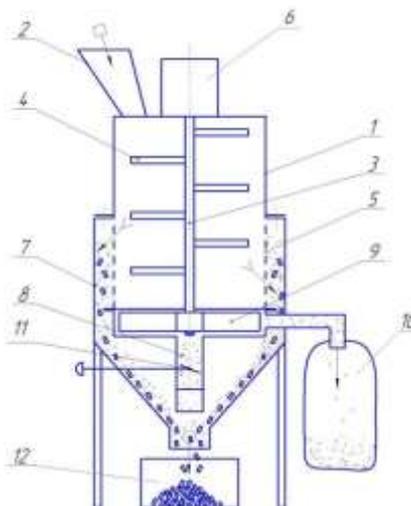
Схема установки для извлечения перги из перговых сотов: 1-камера измельчителя, 2-загрузочная горловина, 3-вал измельчителя, 4-штифт, 5-отверстия, 6-электродвигатель, 7-направляющий кожух, 8- всасывающий кожух, 9-центробежный вентилятор, 10- фильтр для сбора восковой основы соты, 11-заслонка, 12-емкость для сбора перги
